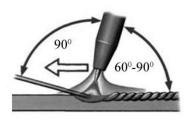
Расположение горелки при аргонодуговой сварке:
